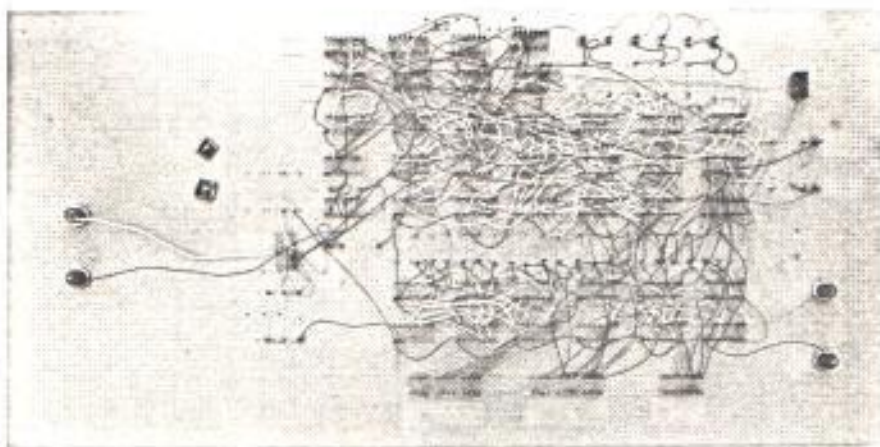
VISTA INFERIOR DEL TABLERO
